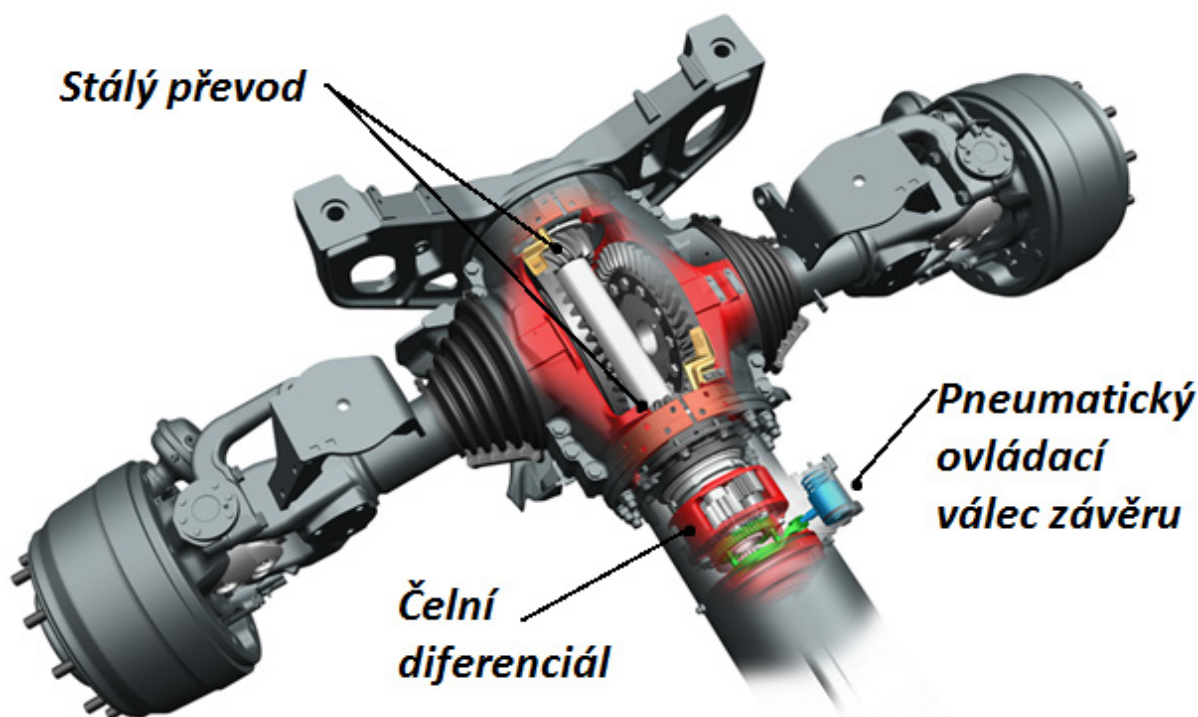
Kuželový diferenciál se závěrem řešeným přesuvnou objímkou [5]
